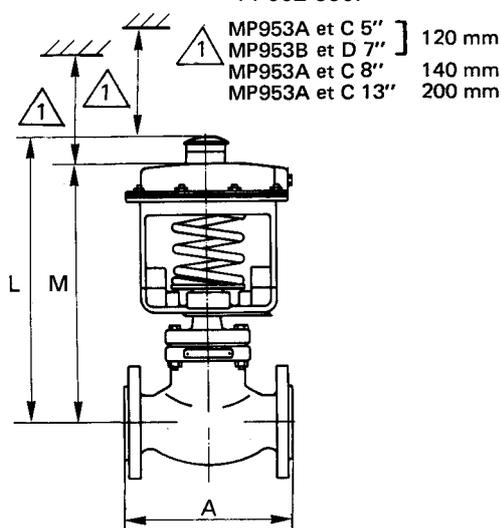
Dimensions en mm avec moteur pneumatique MP953.
